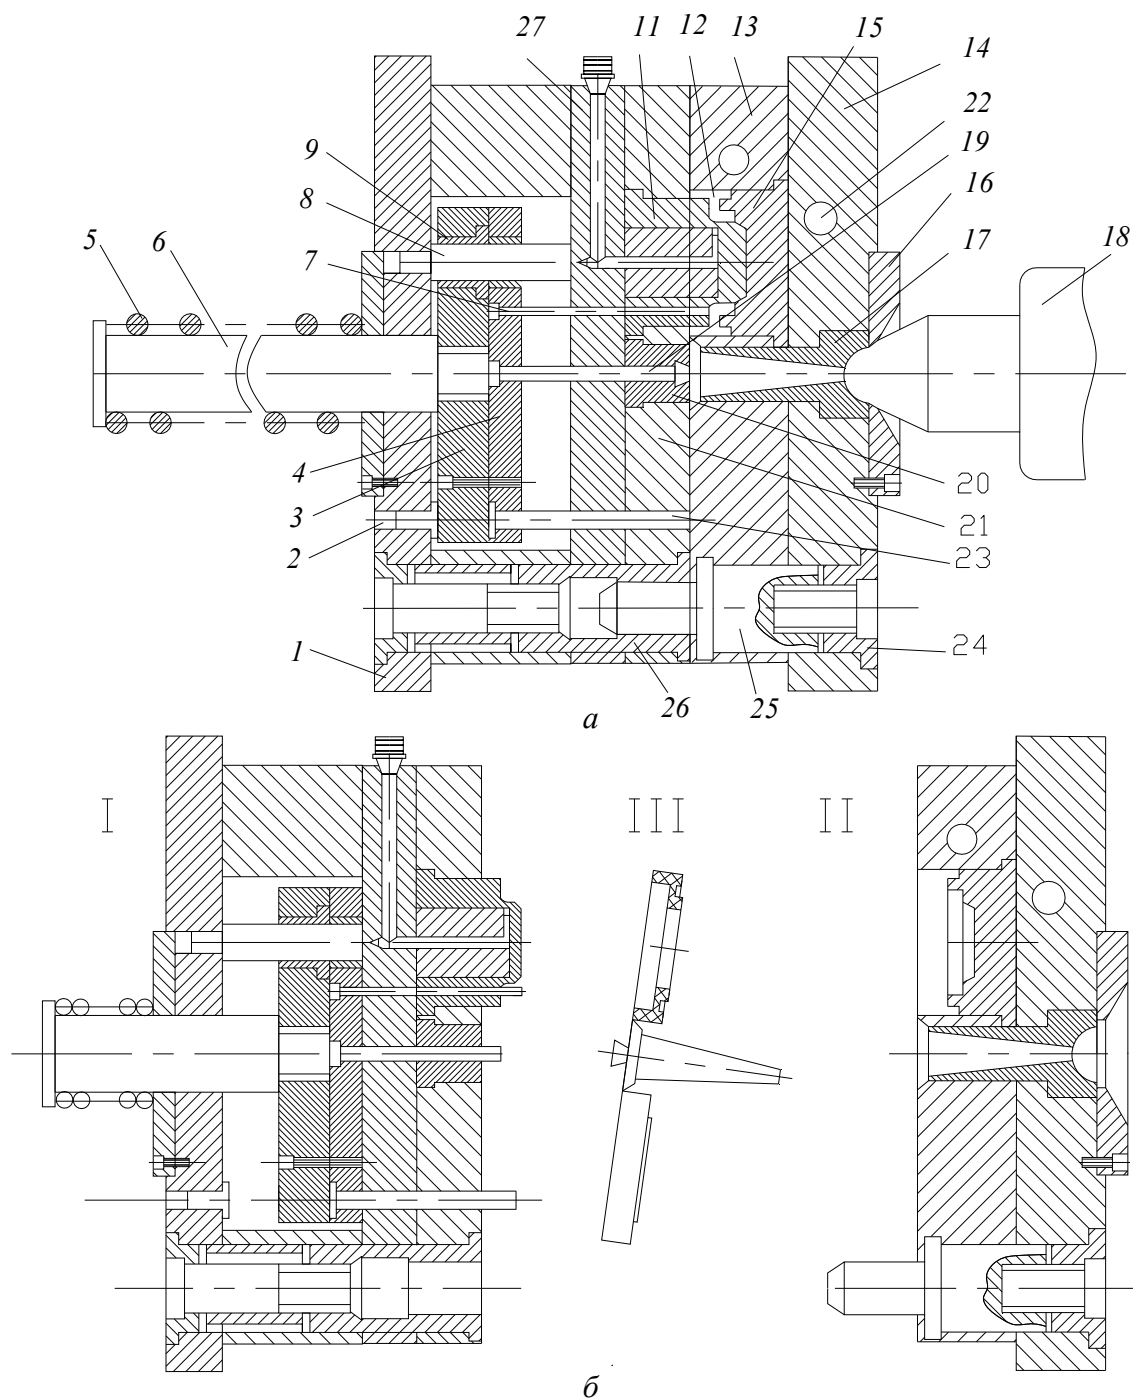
Конструкція типової двогніздової форми для лиття під тиском кільцевої втулки з поліетилену: а – форма зімкнута; б – форма розкрита; I і II – рухома й нерухома півформи; III – виливок; 1 – рухома плита кріплення форми; 2 – упор; 3, 4 – плити виштовхувачів; 5 – пружина; 6 – хвостовик; 7 – виштовхувач; 8, 25 – напрямні колонки; 9, 26 – напрямні втулки; 10 – стійка; 11 – пуансон; 12 – гніздо прес-форми; 13 – обойма матриць; 14 – нерухома плита кріплення прес-форми; 15 – матриця; 16 – фланець; 17 – ливникова втулка; 18 – інжекційний циліндр; 19 – центральний виштовхувач; 20, 24 – втулки; 21 – обойма пуансона; 22 – канал; охолодження; 23 – поворотний штовхач; 27 – проміжна плита
